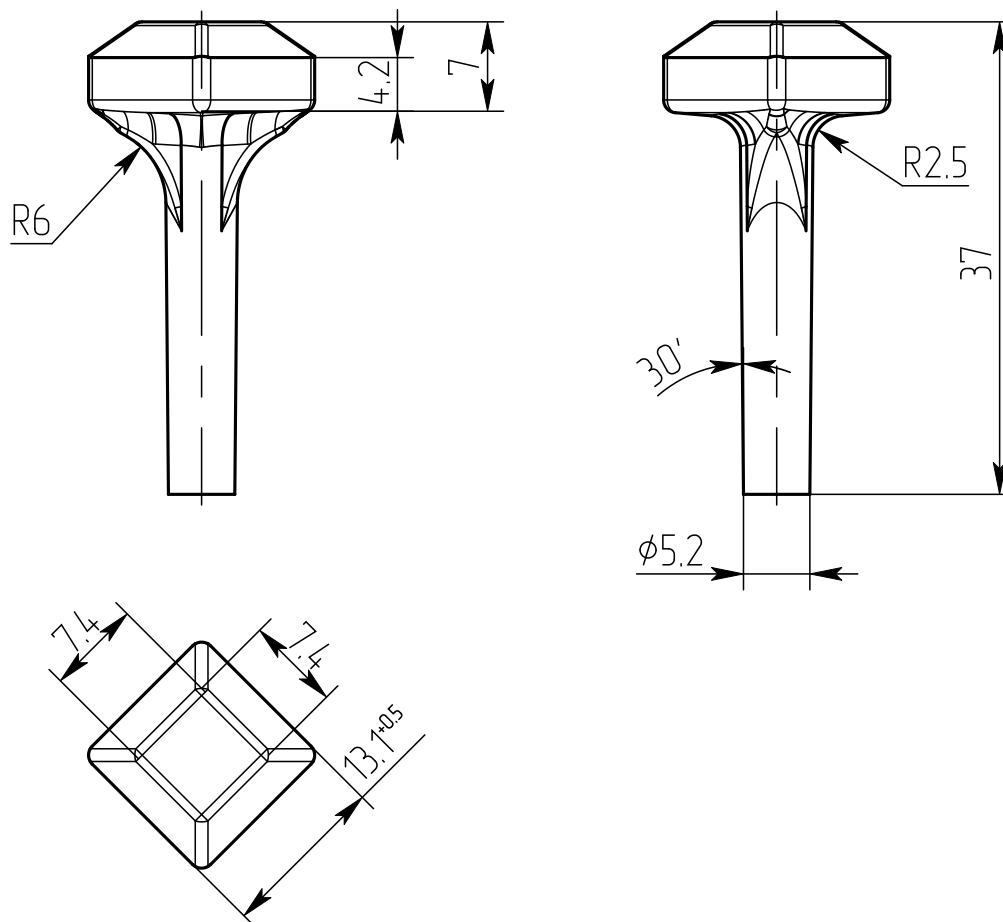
Заготовка с высаженной замковой частью.
